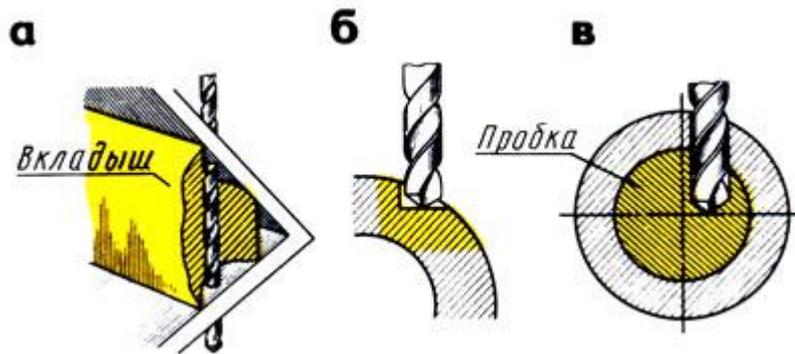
Сверление отверстий: а - в плоскости, расположенной под углом к другой плоскости, б - на цилиндрической поверхности, в - в полых деталях
